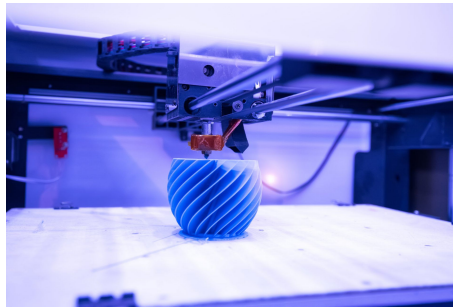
Impresión 3D. Fuente: 3dprintingindustry.
